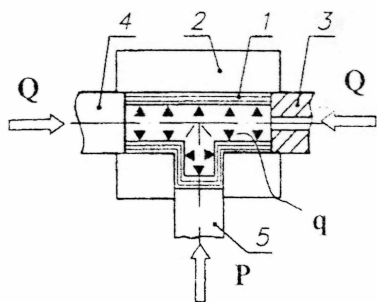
Схема процесса гидроштамповки тройника из трубной заготовки: 1 – тройник; 2 – разъемная матрица; 3, 4 – осевые пуансоны; 5 – пуансон противодавления
